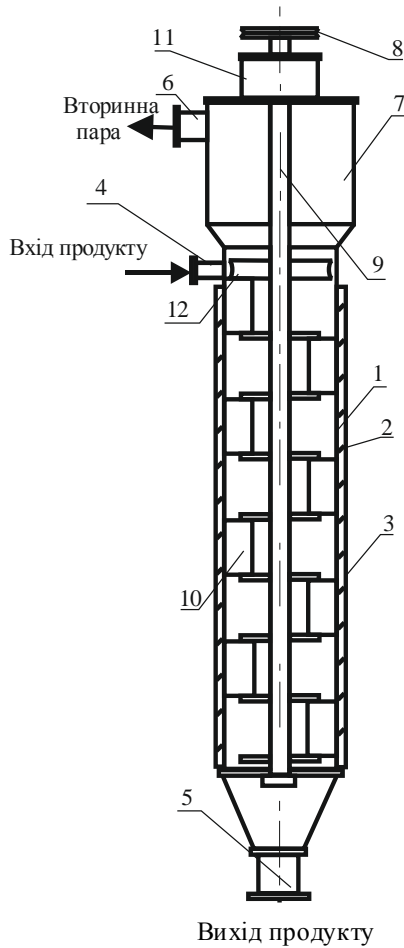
Роторний плівковий апарат: 1 – корпус апарата; 2 – гнучкий плівковий резистивний електронагрівач випромінювального типу; 3 – ізоляційний матеріал; 4 – патрубок входу продукту; 5 – патрубок виходу продукту; 6 – вихід вторинної пари; 7 – сепаратор; 8 – привідний шків; 9 – вал ротора; 10 – шарнірна лопать; 11 – система герметизації обертового вала; 12 – розподільне кільце
